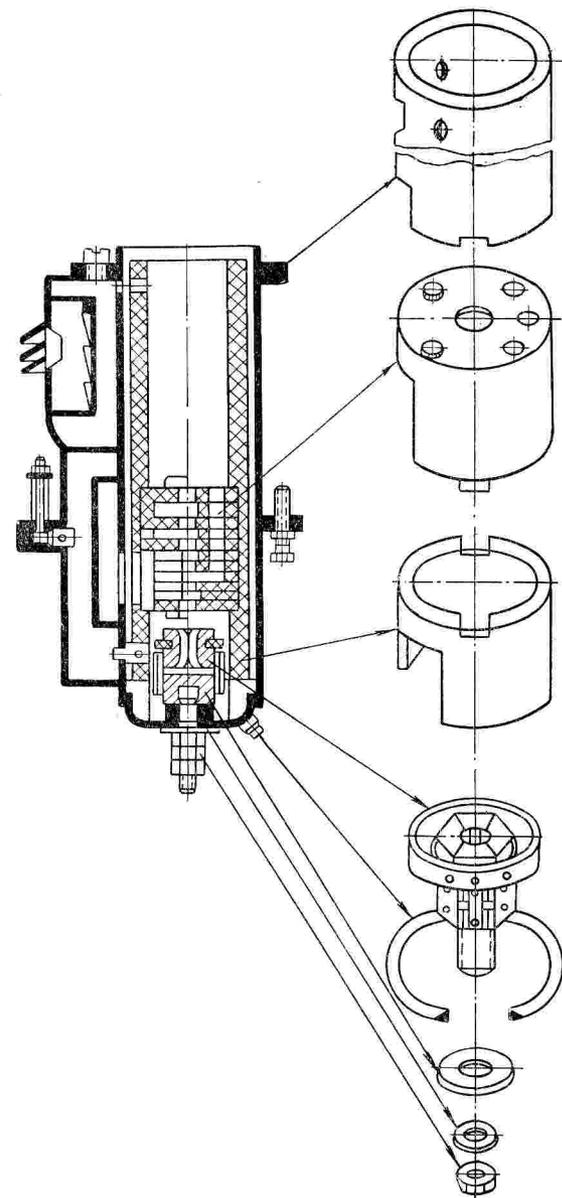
Порядок сборки цилиндра выключателя типа ВМГ-133
